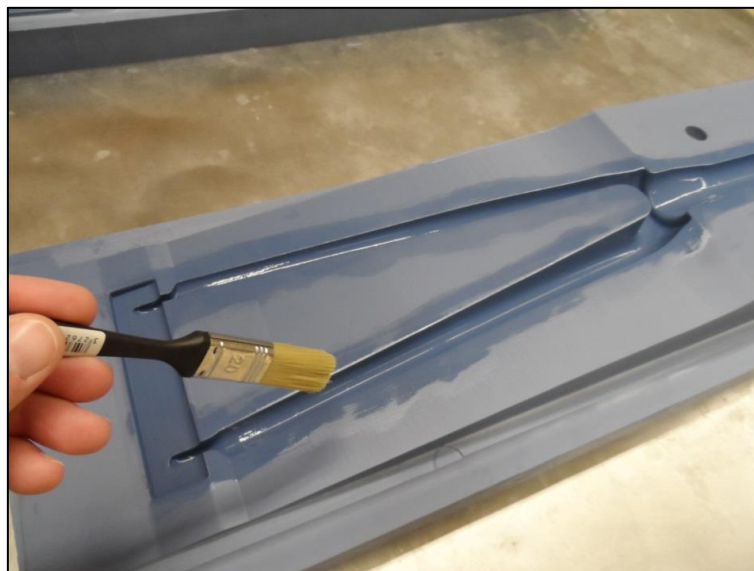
Revestimento multicamadas com desmoldante SB 680.
